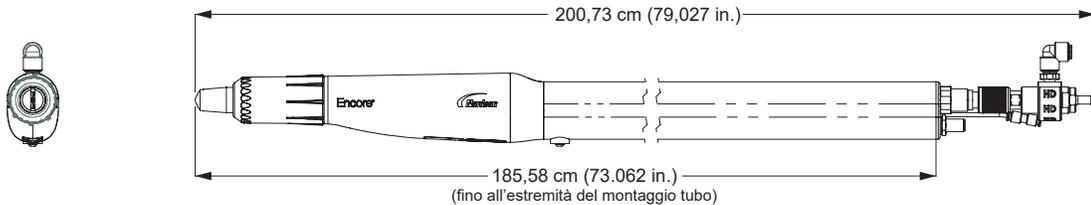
Dimensioni e pesi della pistola a spruzzo
